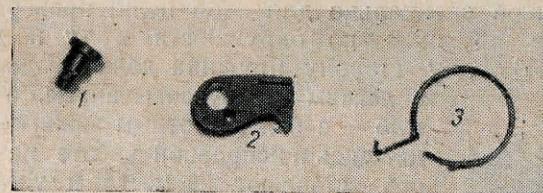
Винт, фиксирующий крючок и пружина механизма передвижения пленки
